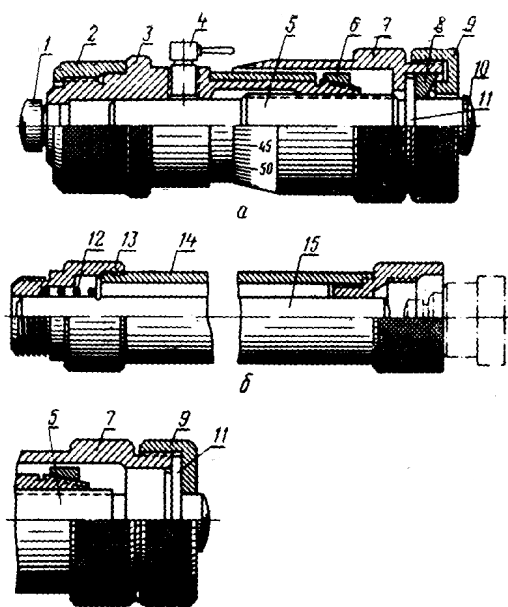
Микрометрический нутромер: 1 и 10 – сферические наконечники; 2 – предохранительная гайка; 3 – стебель; 4 – стопорный винт; 5 – микровинт; 6 – регулировочная гайка; 7 – барабан; 8 – разрезное кольцо; 9 – установочный колпачок; 11 – буртик; 12 – пружина; 13 – предохранительная головка; 14 – предохранительная трубка; 15 – удлинитель
